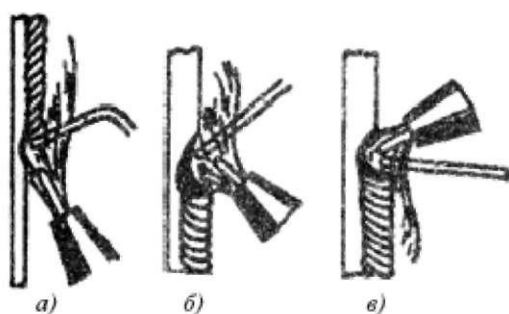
Сварка вертикальными швами: а - сверху вниз; б, в - снизу вверх
